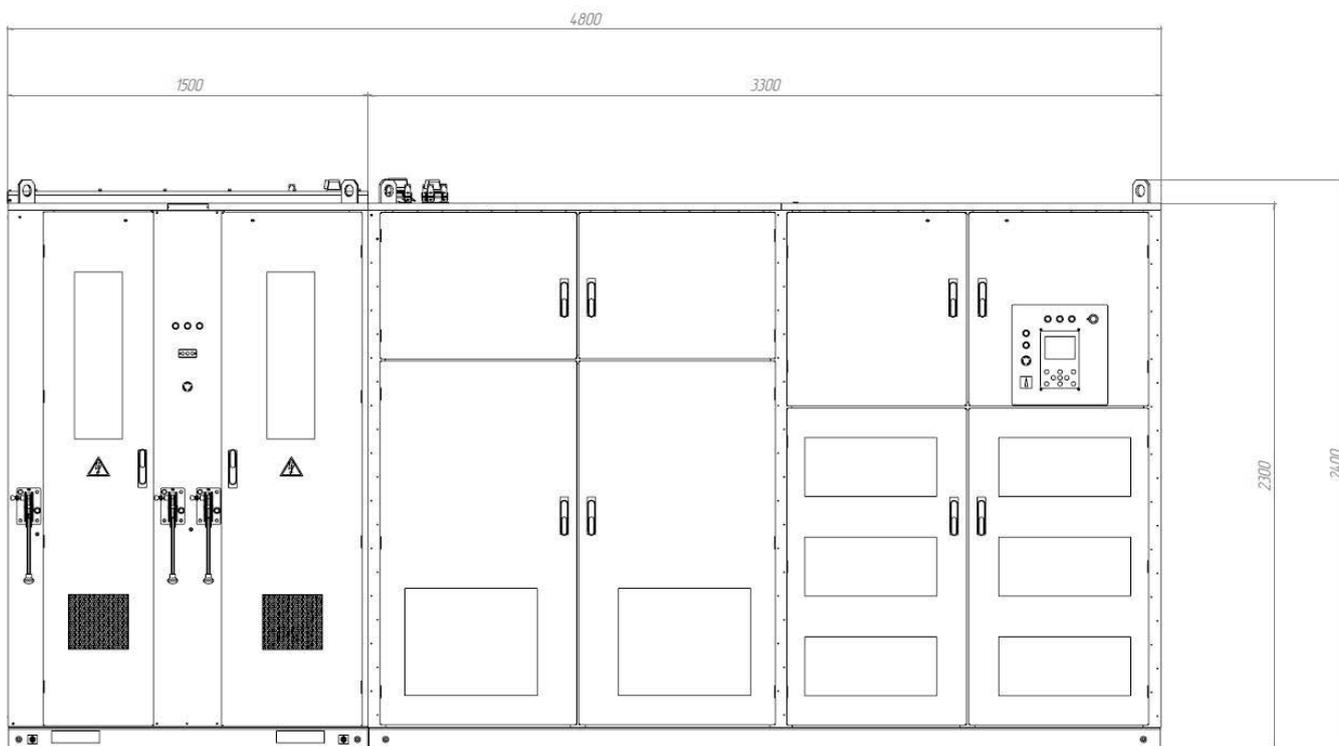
АТ27-М40...М63-6/6-XXXXXX-С-43. Вид спереди
